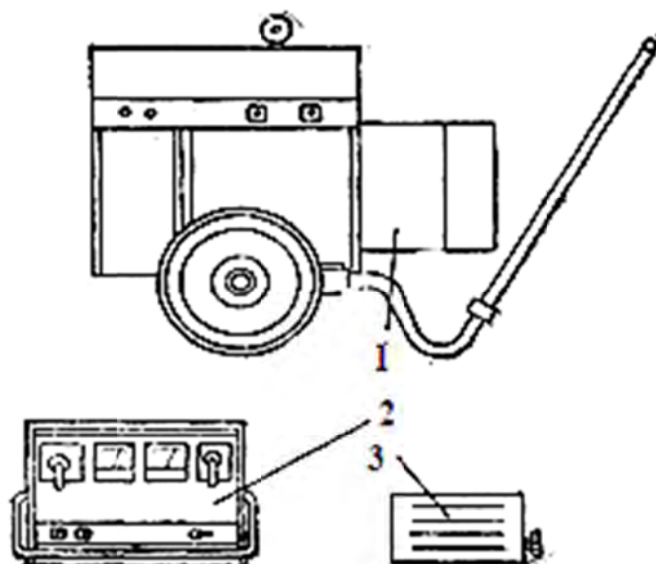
Сварочно-зарядная установка типа УДЗ-103У2:
